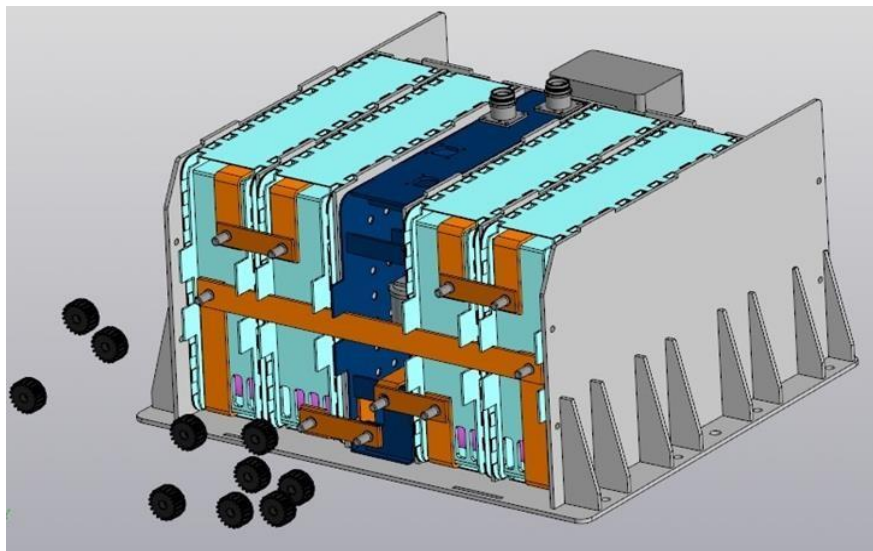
3D-модель сборки высоковольтной аккумуляторной батареи
